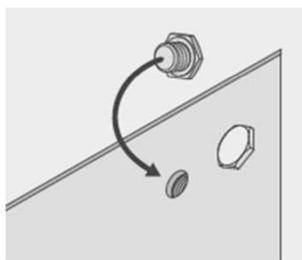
Befestigungszubehör entfernen, Innengewinde auf Verschmutzung prüfen ggf. reinigen
